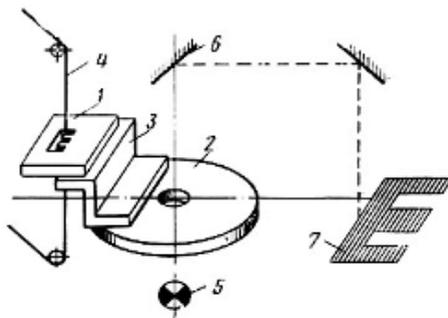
Схема копировально-вырезного станка: 1–электрод-деталь; 2–координатный стол; 3–приспособление для крепления детали; 4–электрод-проволока; 5–подсвет; 6–оптическая система; 7–копир-экран
